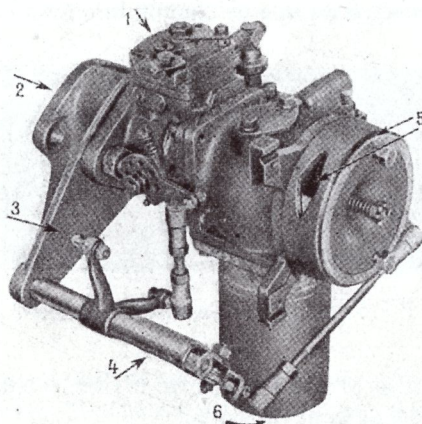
Mélangeur du moteur Latil M. 3 G.
